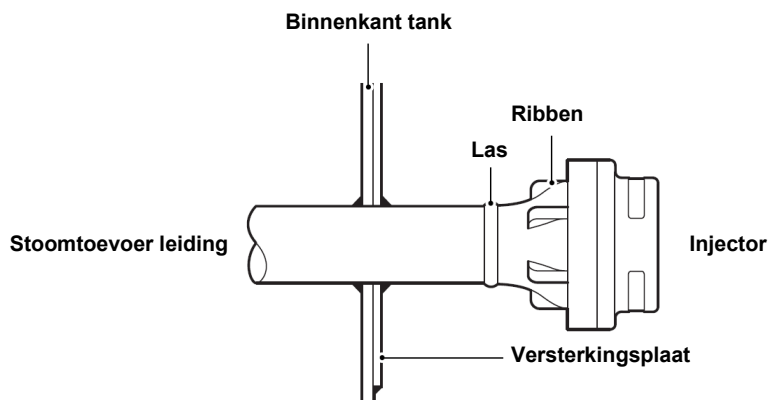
IN25M/IN40M – Typische installatie met butt weld door de tankwand op een leiding
